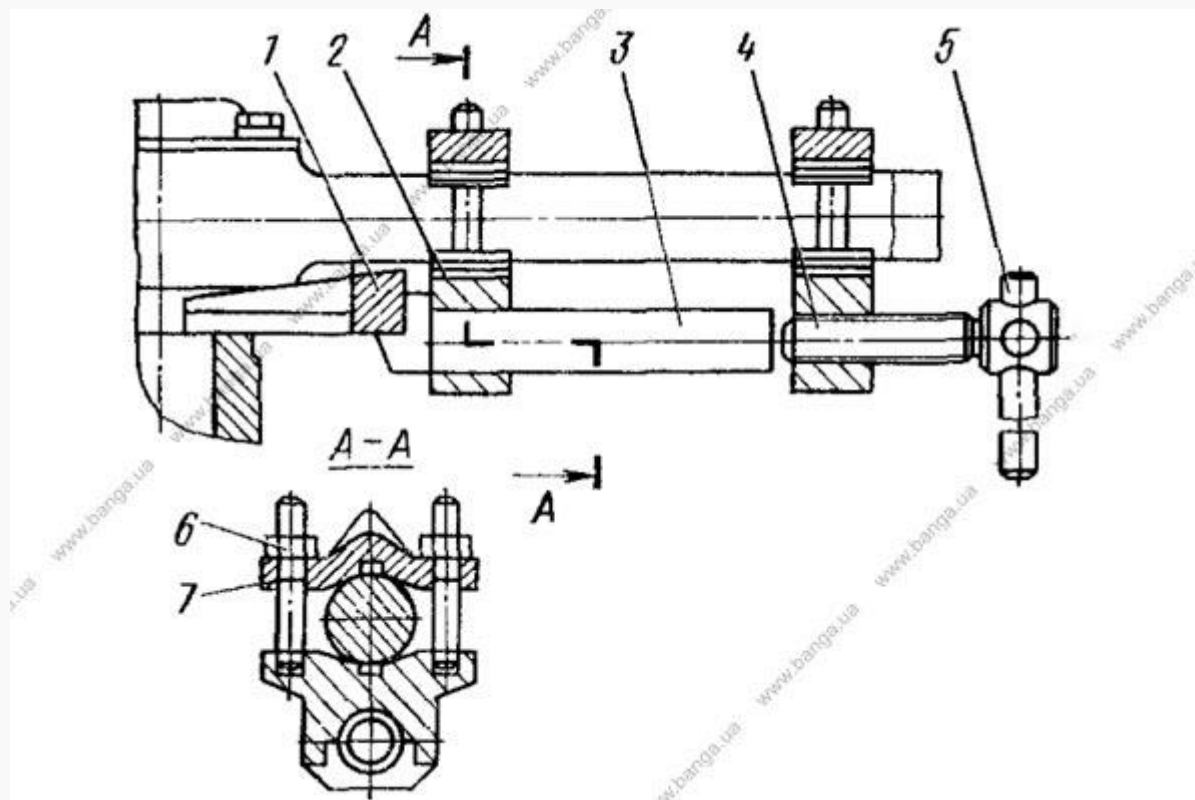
Снятие реактивной штанги съемником И-801.42.000: 1— клин, 2—корпус; 3—наконечник; 4—винт; 5—рукоятка; 6—гайка; 7— планка
